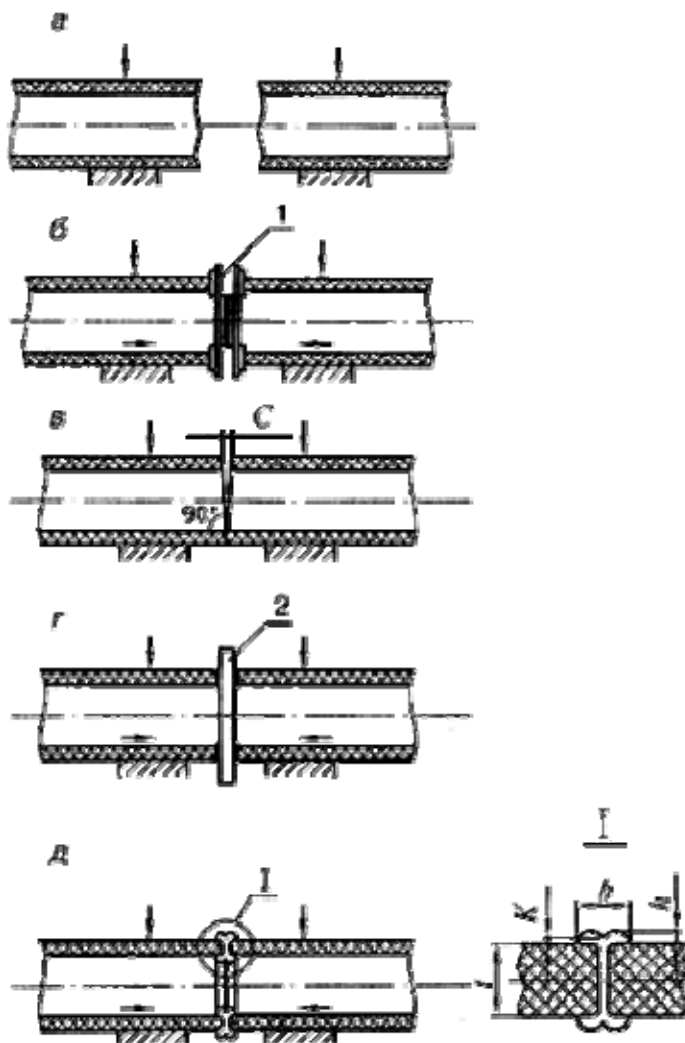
Последовательность процесса сборки и сварки встык полиэтиленовых труб
